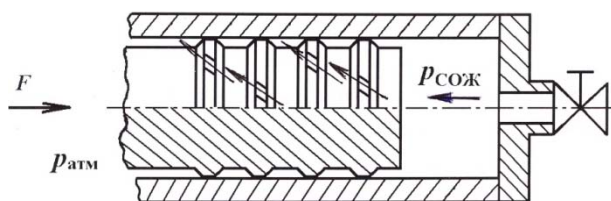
Схема подачи СОЖ к дорнующим зубьям со стороны обрабатываемого отверстия
